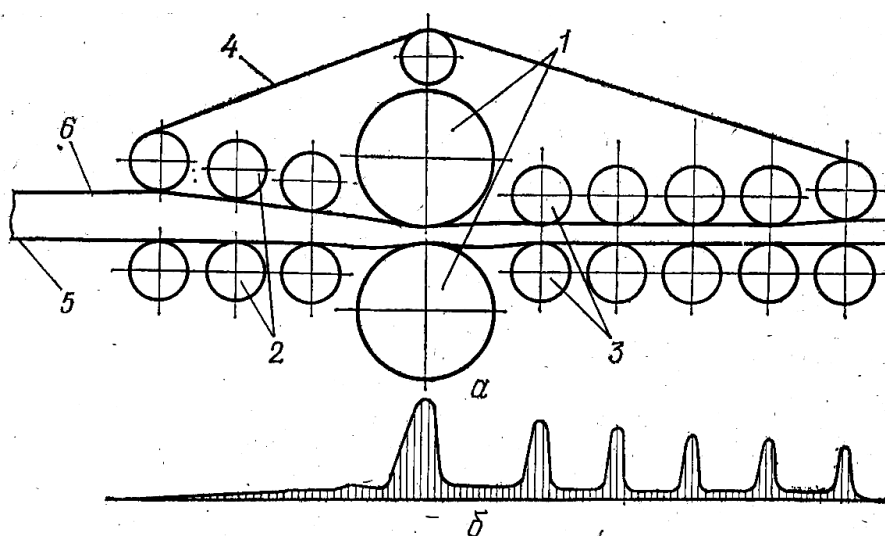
Схема ленточно-валкового прессы для подпрессовки (а) и эпюра давления подпрессовки (б): 1 – прессующие барабаны; 2 – валки зоны уплотнения; 3 – валки зоны выдержки; 4, 5 – соответственно верхняя и нижняя ленты; 6 – подпрессовываемый ковер
